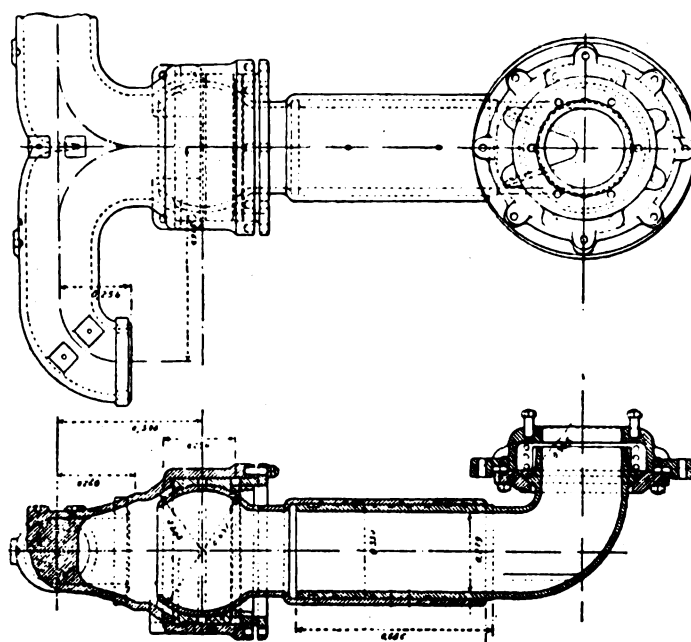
e 10. — Tubo d'introduzione nei cilindri B. P. - Pianta ed elevazione.
